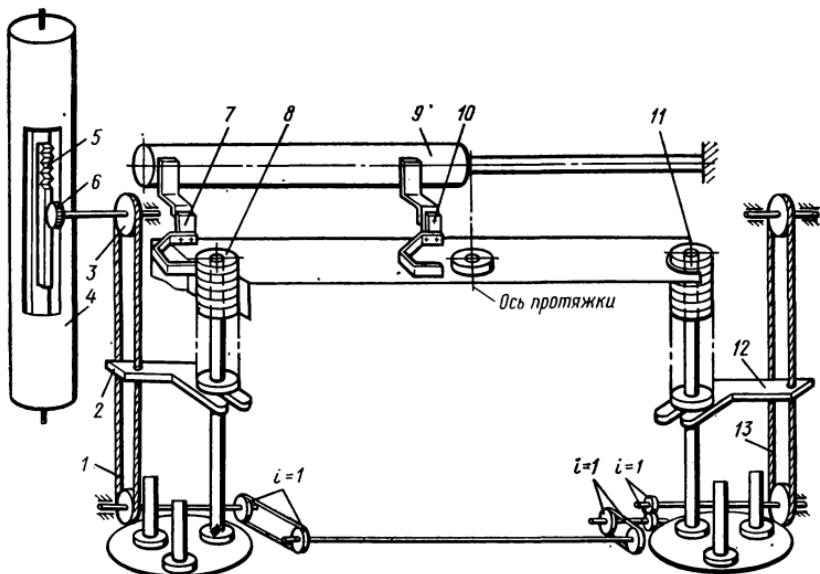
Автоматизированное загрузочно-разгрузочное приспособление для вертикально-протяжных станков:
